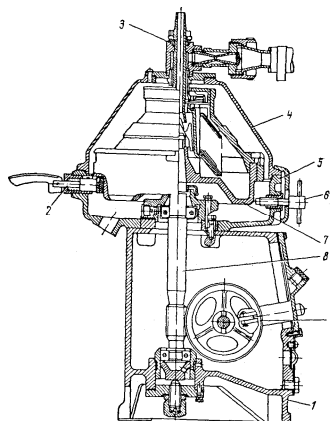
Сепаратор-молокоочисник напівзакритого типу з ручним вивантаженням осаду: 1 – корпус станини; 2 – гальмо; 3 – приймально-вивідний пристрій; 4 – кришка сепаратора; 5 – чаша станини; 6 – стопор барабана; 7 – барабан; 8 – вертикальний вал (веретено); 9 – зубчасте колесо горизонтального вала
